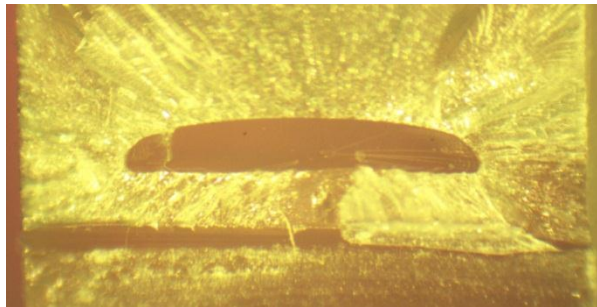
Superficie de fractura de una probeta con entalla incorrecta.
